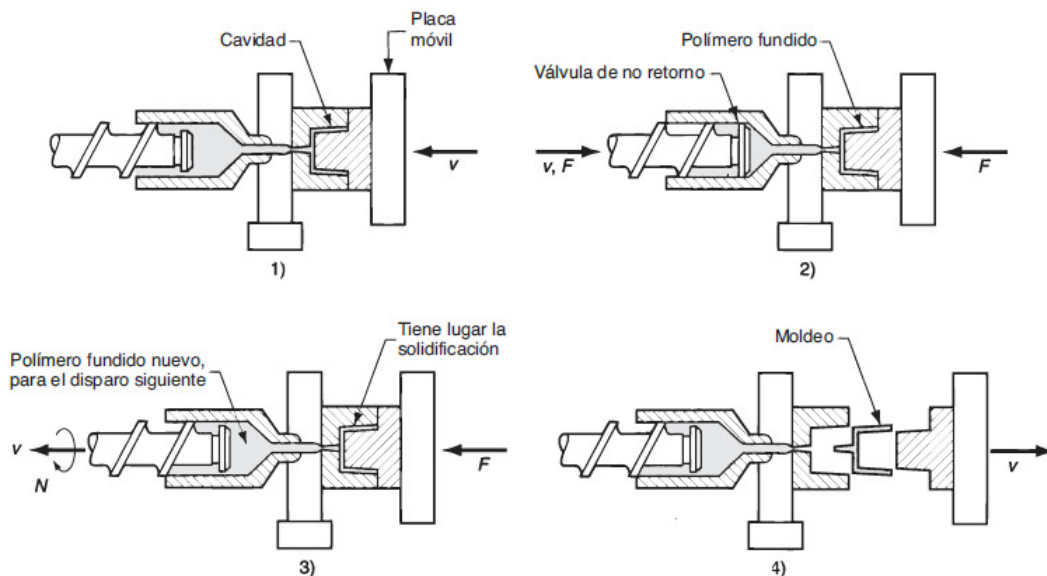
Ciclo común de moldeo: 1) Molde cerrado, 2) Se inyecta fluido a la cavidad, 3) Se retrae el tornillo y 4) Se abre el molde y la pieza se expulsa [1].
